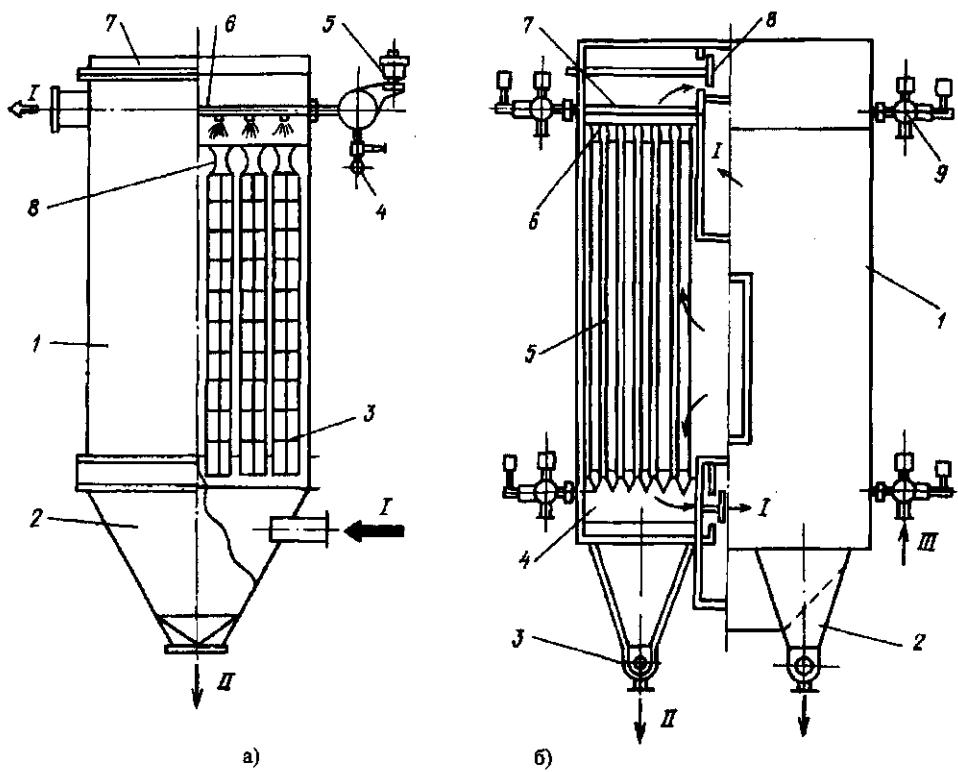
Рукавные фильтры типа ФРКИ и ФРКДИ:
